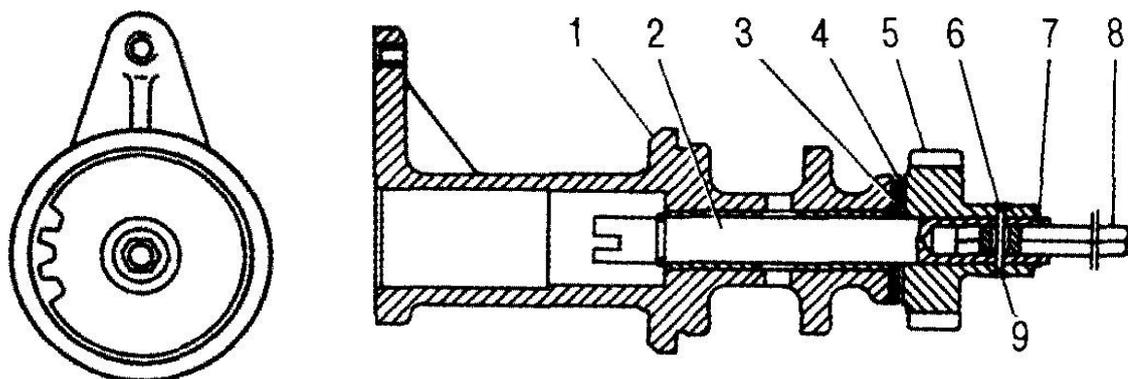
Привод датчика-распределителя зажигания и масляного насоса: 1 - корпус привода; 2 - валик привода; 3,4- упорные шайбы; 5 - ведомая шестерня привода; 6 - пружинное кольцо; 7 - стопорное кольцо; 8 - валик привода масляного насоса; 9 - штифт
